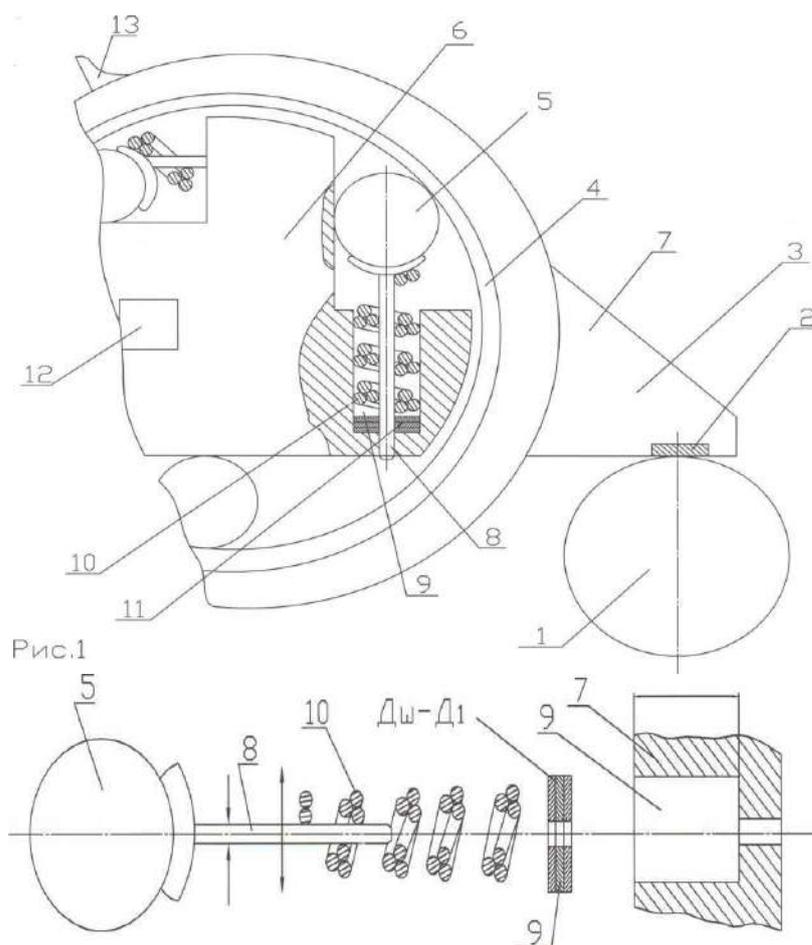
Схема узла толкателя импульсного вариатора
